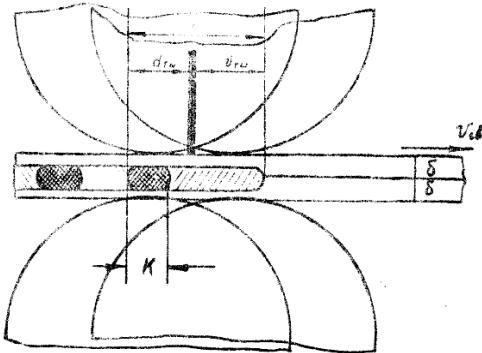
Схема шовной сварки и расчетные размеры сварного соединения
